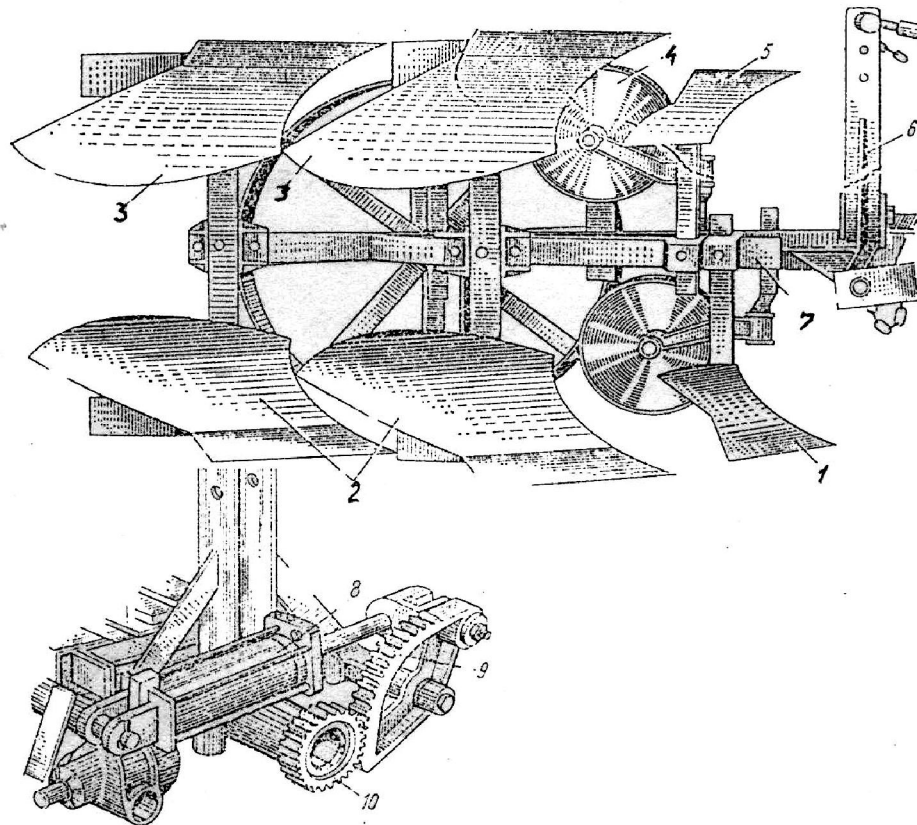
Плуг оборотний начіпний ПОН-2-30:
